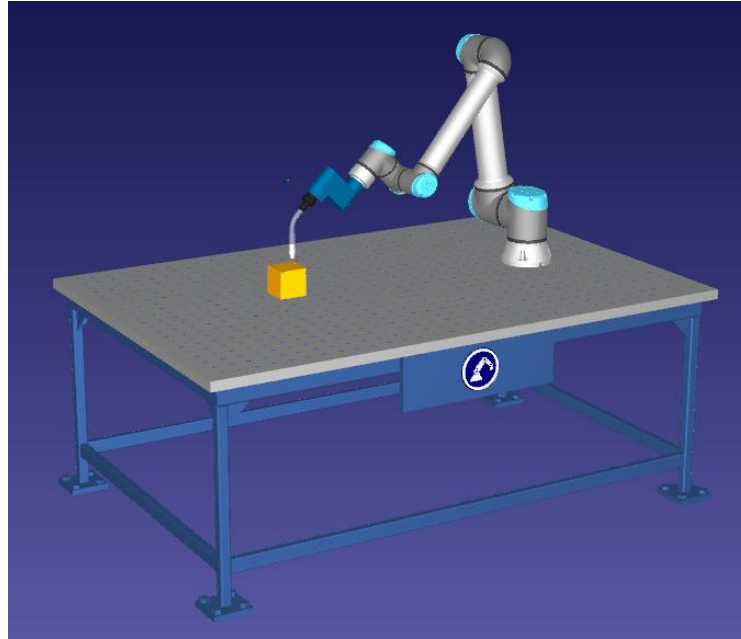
Idealização de uma célula de soldadura de um robô colaborativo
